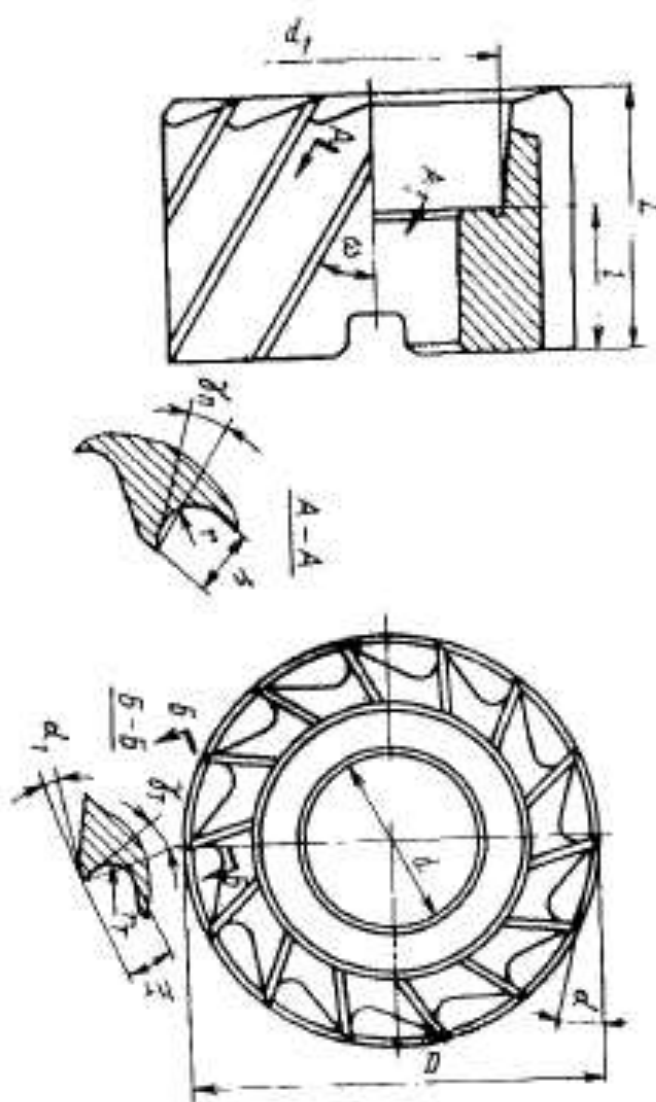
Фреза торцовая насадная 2210-0073
